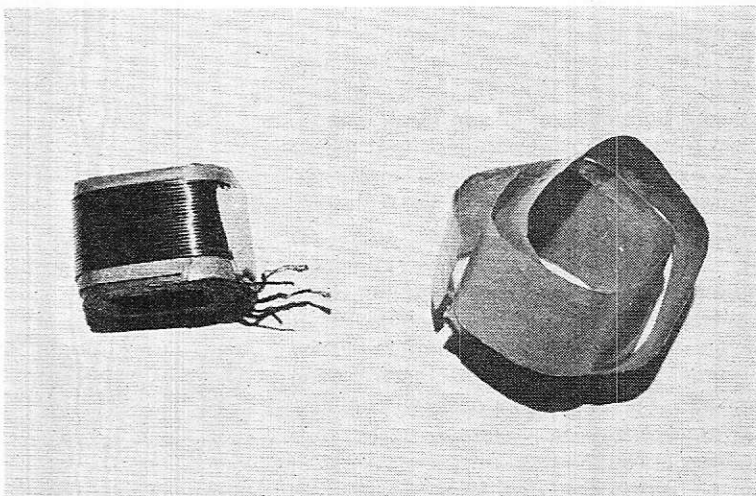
L'enlèvement du papier de protection laisse apparaître un premier enroulement.
